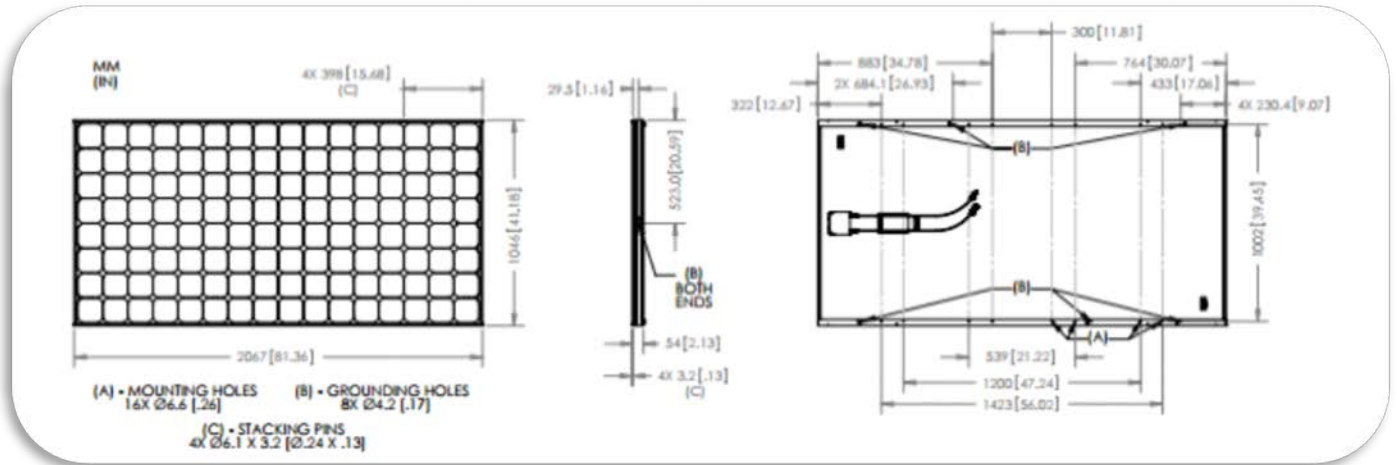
Detalles de las dimensiones del módulo (Fuente: Next Energy).
